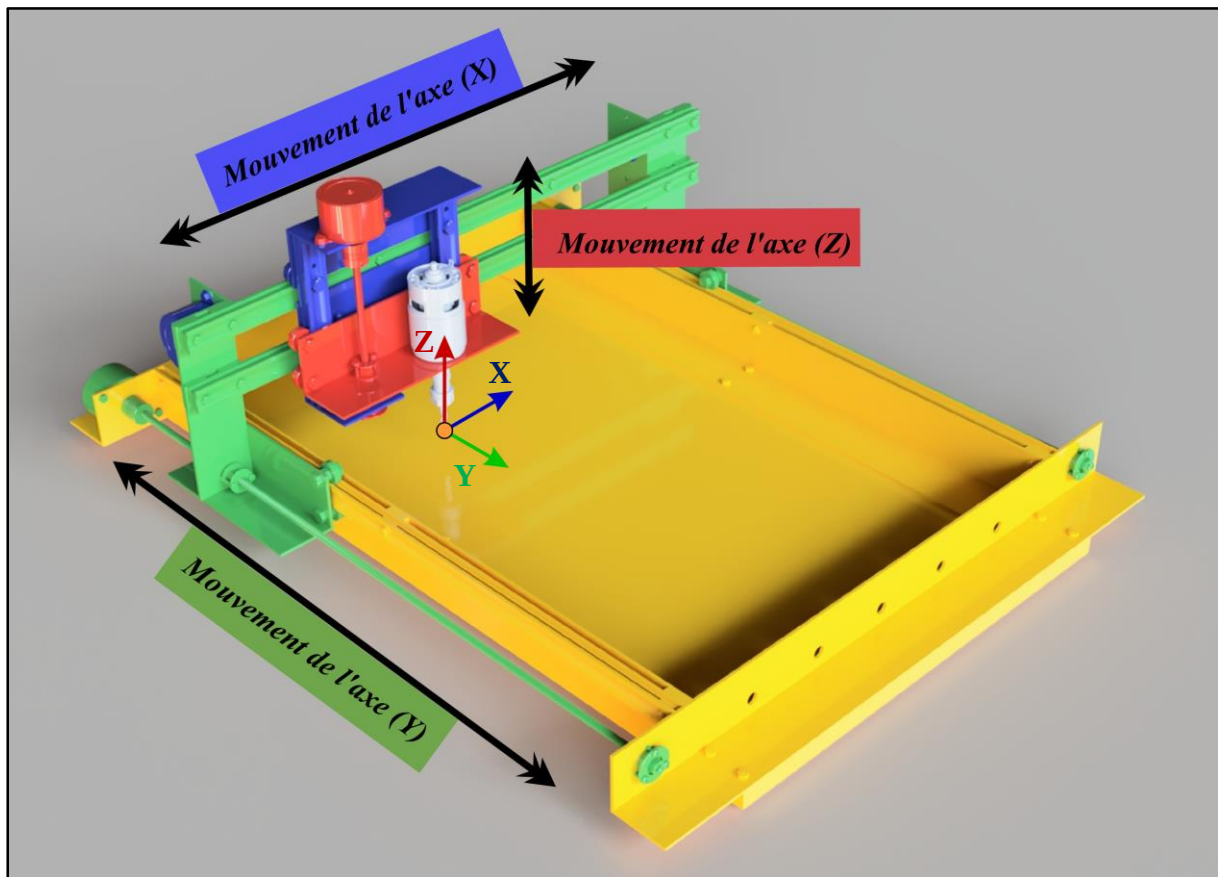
Limites de mouvement de la machine CNC à 3 axes.
